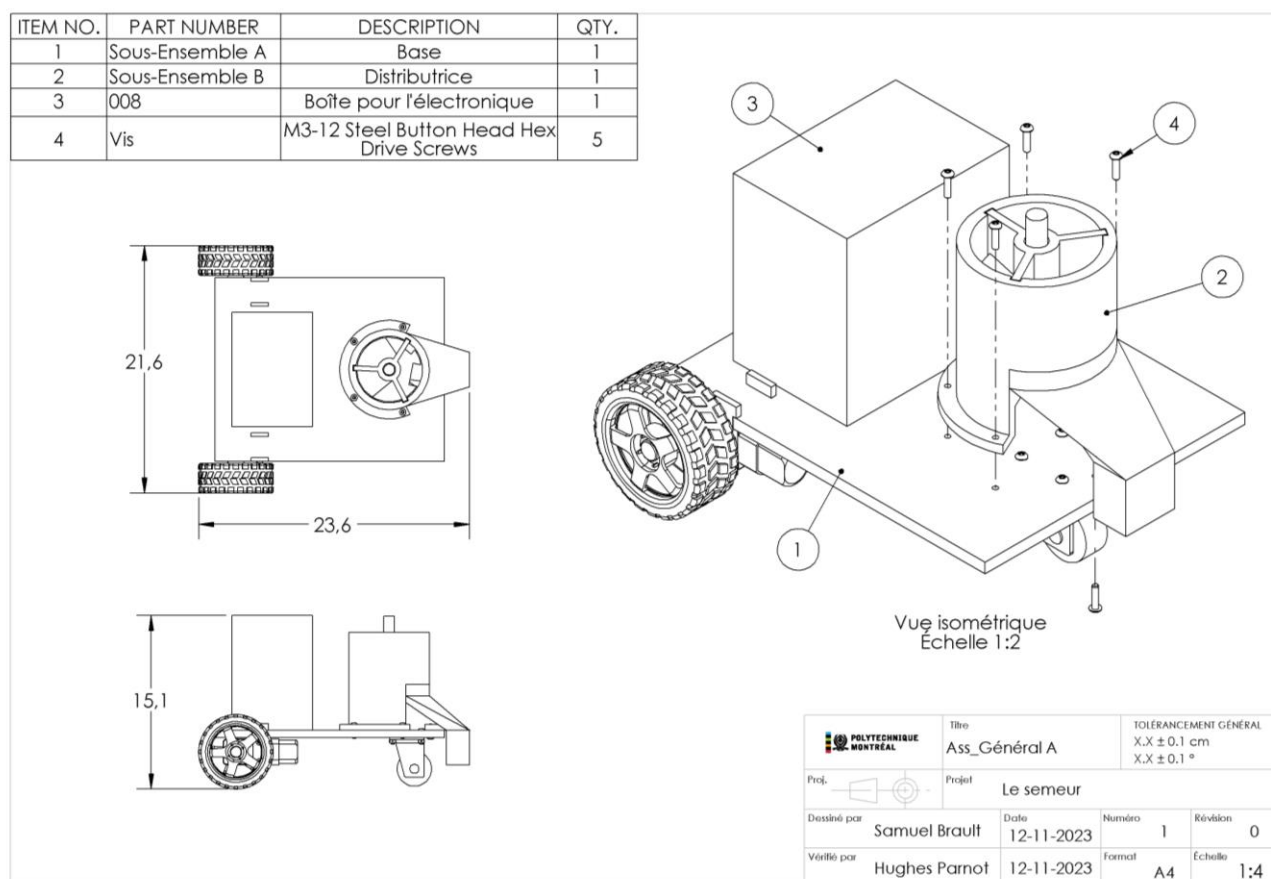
Dessin d'assemblage de l'Assemblage Général A
